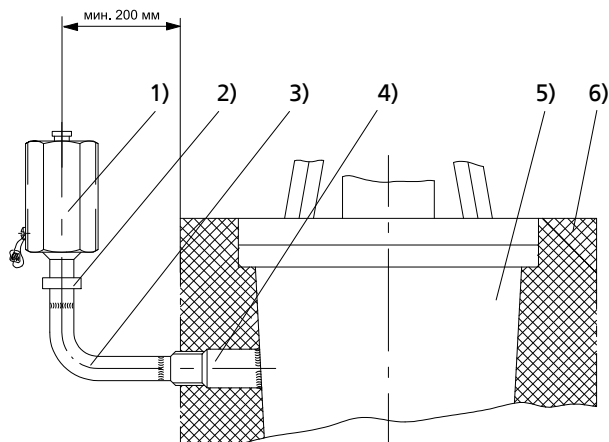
Устройство защиты корпуса от избыточного давления UGS/UGSV на запорной задвижке
